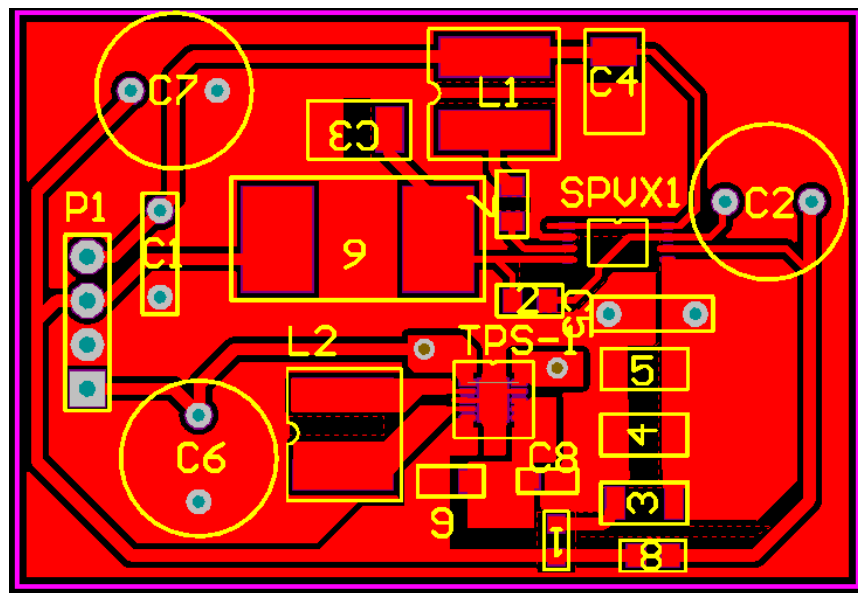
PCB diseñada para las pruebas del prototipo en Altium Designer.
